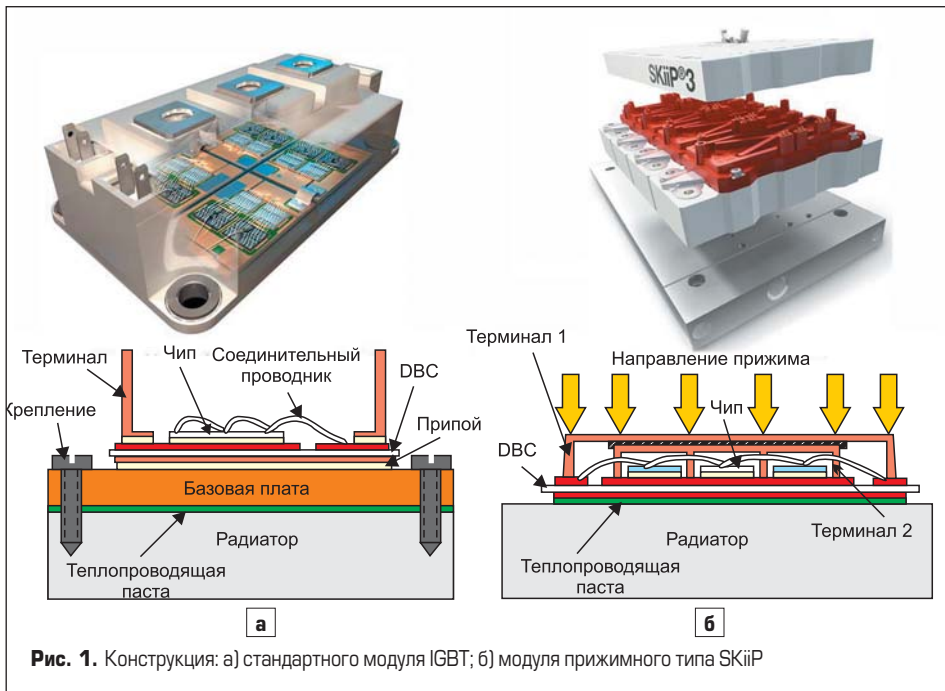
Конструкция: а) стандартного модуля IGBT; б) модуля прижимного типа SKiiP
